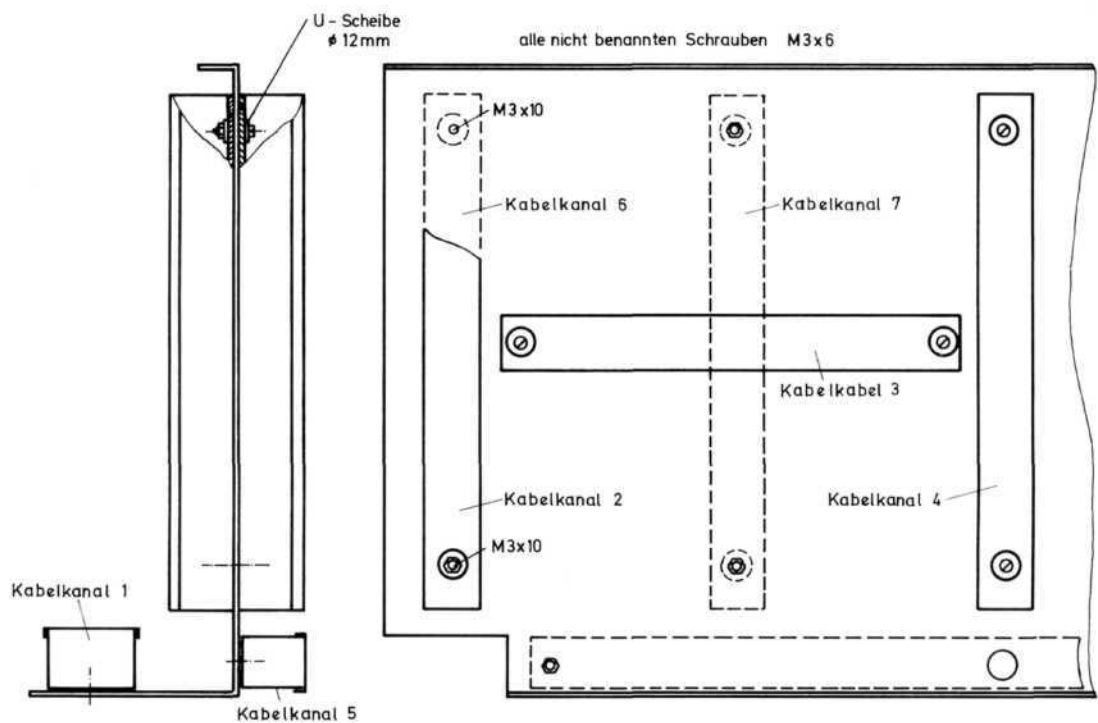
Anschrauben der Kabelkanäle 1 ... 7
